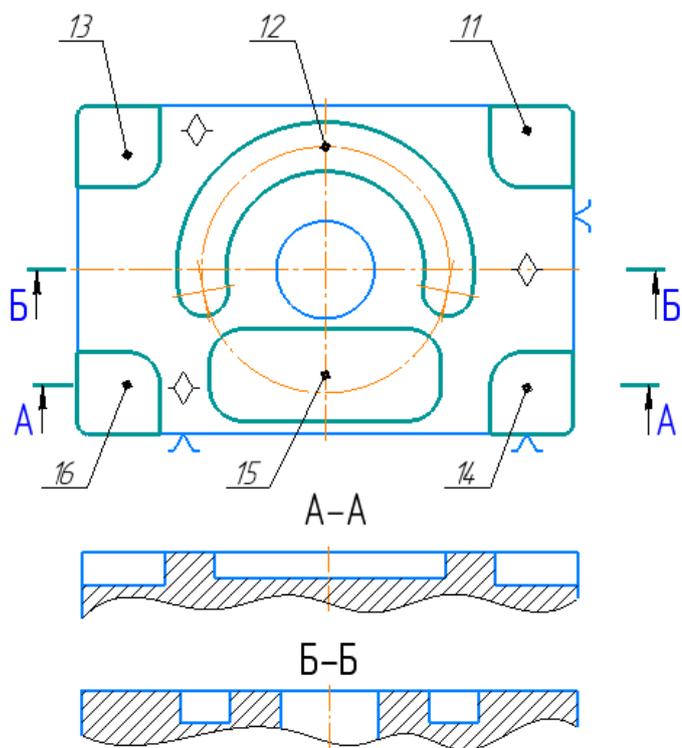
Эскиз фрезерной с ЧПУ операции
